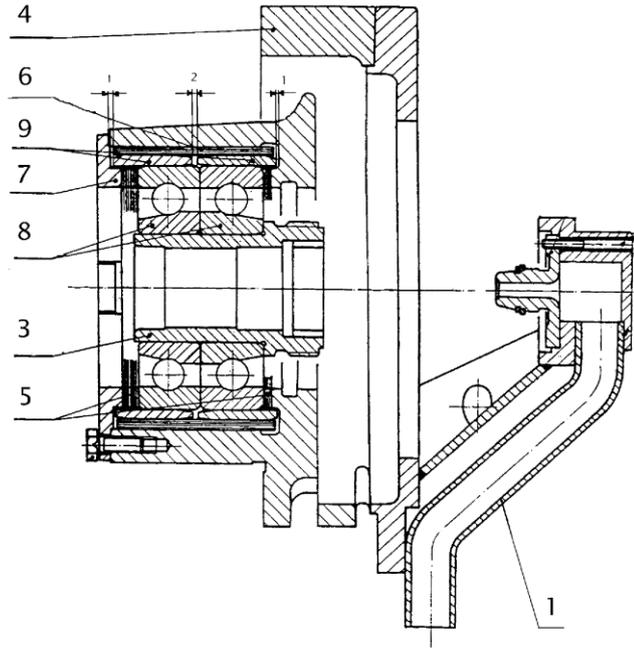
Подшипниковая опора компрессора турбокомпрессора PDH50 ZV-D
